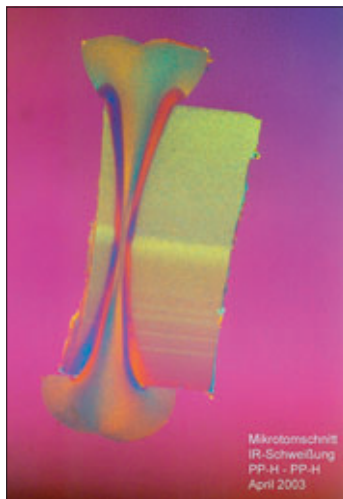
Mikrotomschnitt an einer gebrochenen IR-Schweißprobe aus PP-H
